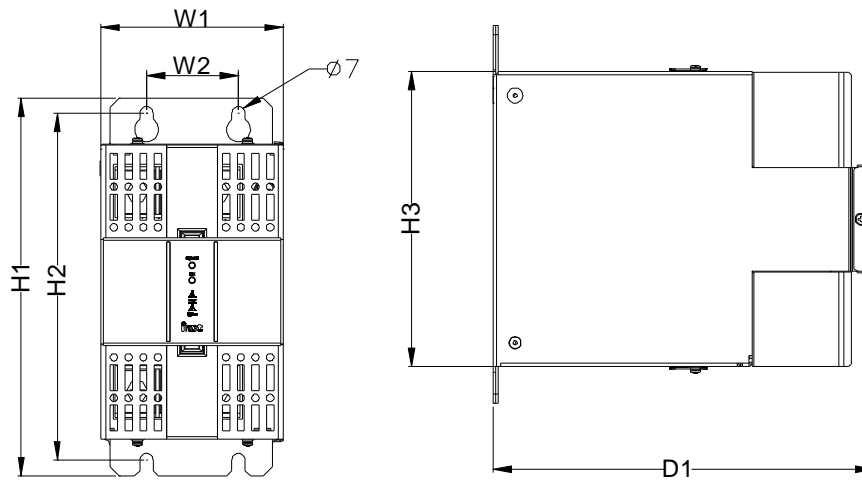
Чертеж для настенного монтажа VUB600-037-4/ VUB600-075-4
